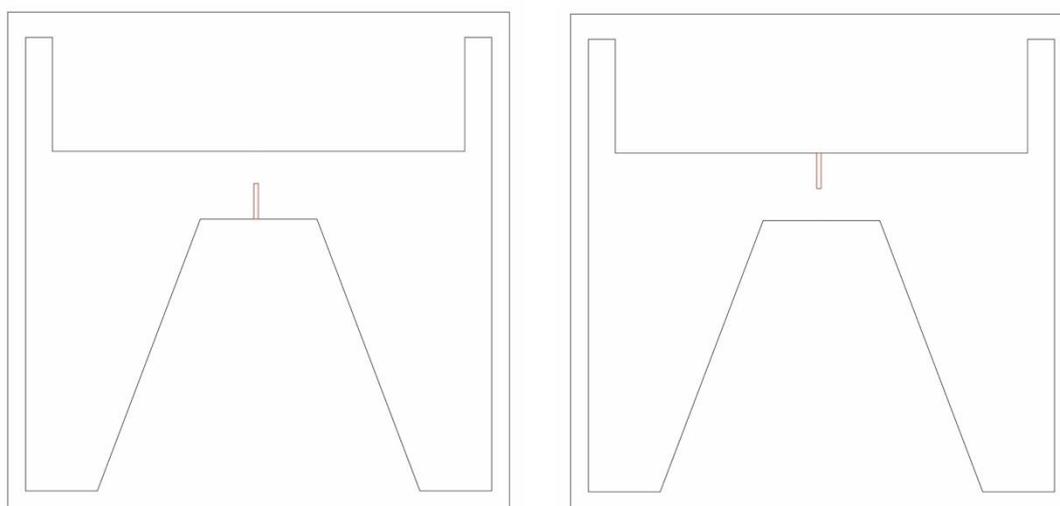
DIBUJOS EN ILLUSTRATOR PARA PLANTILLA DE ELEVACMACETEROS. FUENTE: PROPIA
